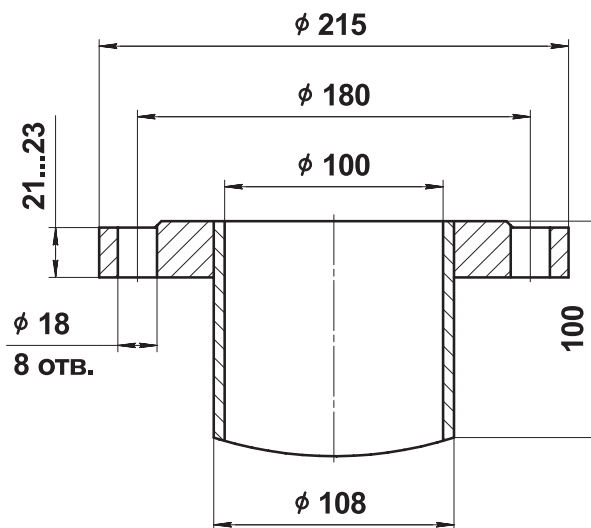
Размеры приварного патрубка на давление до 1,6 МПа
